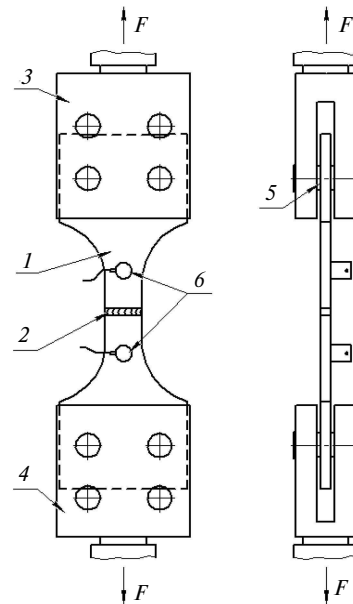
Схема нагружения образца: 1 — образец; 2 — сварной шов; 3 — верхний захват нагружающего устройства; 4 — нижний захват нагружающего устройства; 5 — палец; 6 — ПАЭ
